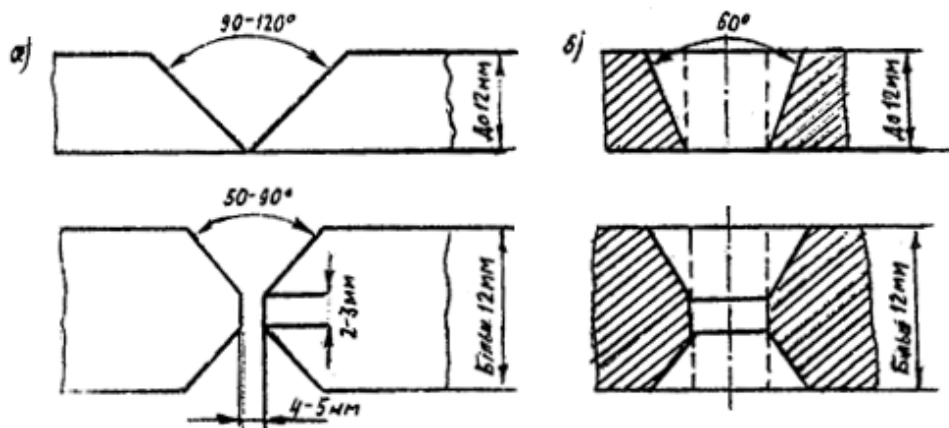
Підготовка тріщини (а) і отвору (б) до зварювання
